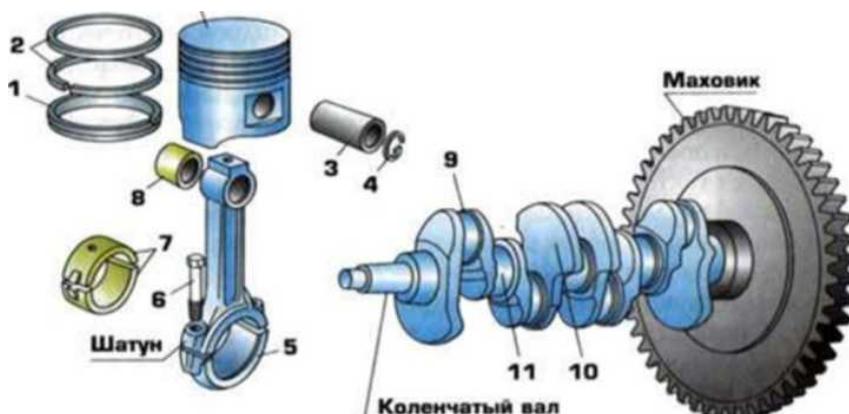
Детали кривошипно-шатунного механизма: 1 – маслоъемное кольцо; 2 – компрессионные кольца; 3 – поршневой палец; 4 – стопорное кольцо; 5 – крышка шатуна; 6 – болт; 7 – вкладыши; 8 – втулка; 9 – шатунная шейка; 10 – противовес; 11 – коренная шейка
